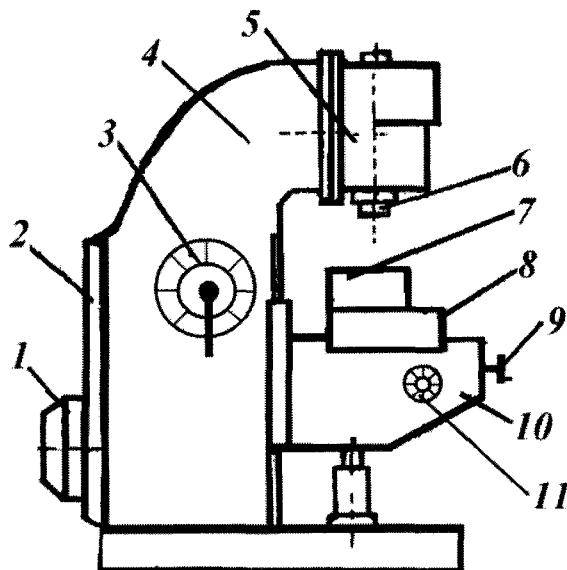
Общий вид фрезерного станка модели СФ 35-010
